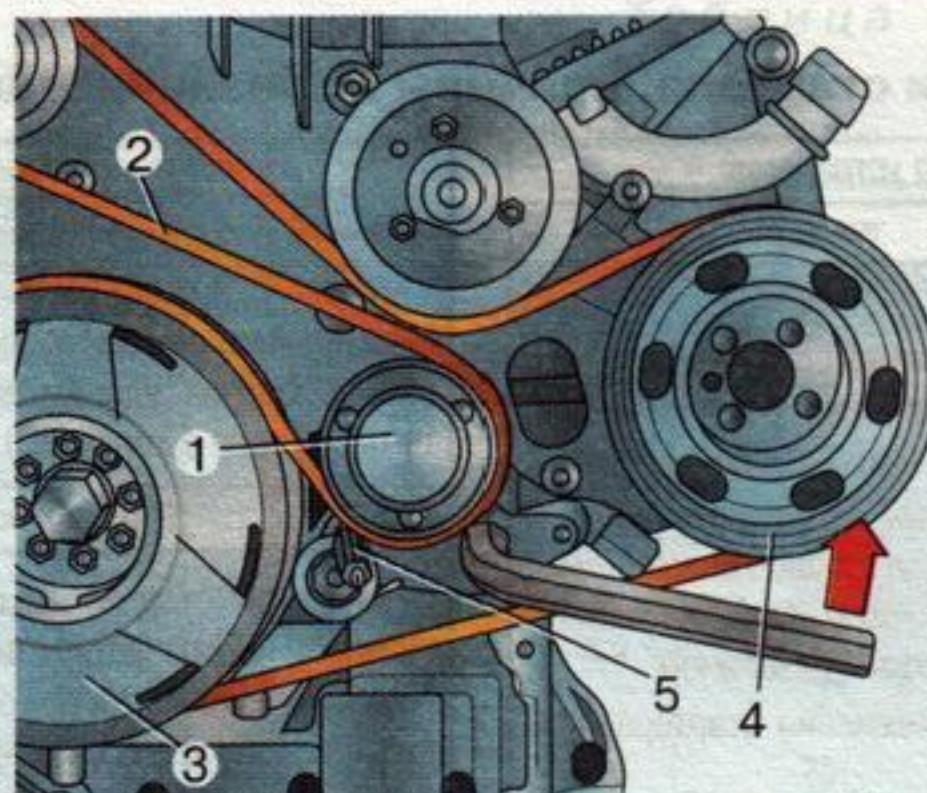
Механизм натяжения ремня привода агрегатов дизельного двигателя рабочим объемом 2,5 л: 1 – натяжной ролик; 2 – ремень привода агрегатов; 3 – шкив коленчатого вала; 4 – шкив насоса гидроусилителя рулевого управления; 5 – штифт
